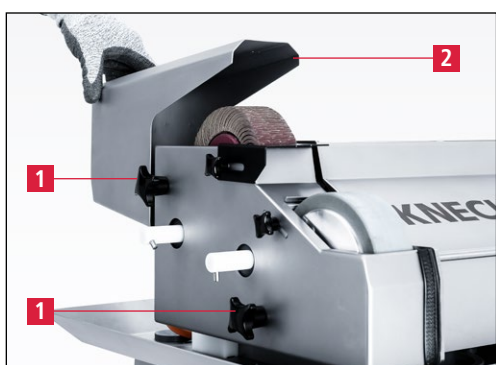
Монтаж защитного кожуха и установка защиты от брызг
